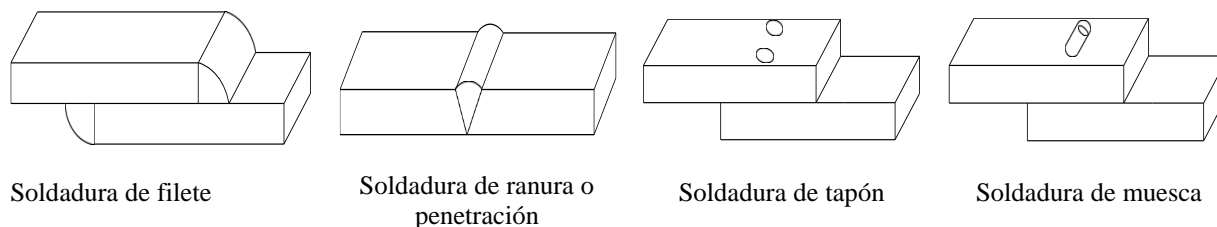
4 Tipos de soldaduras estructurales
